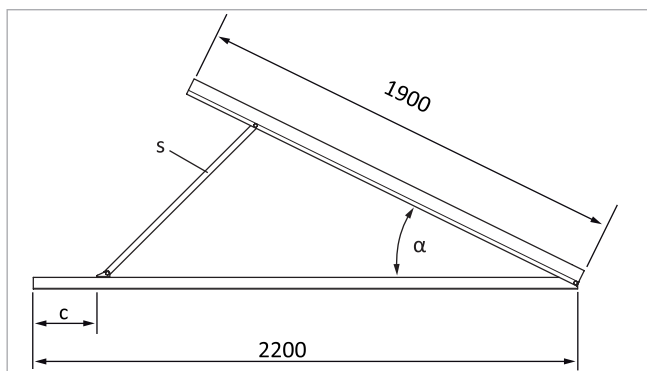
Soporte para tejado plano, dimensiones y ángulo de colocación
